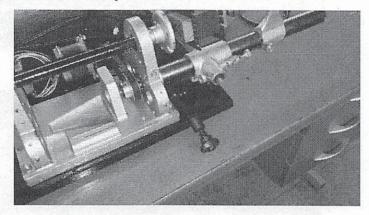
Peça de latão que engrena no fuso com desgastes, produzindo folga no desandador.
